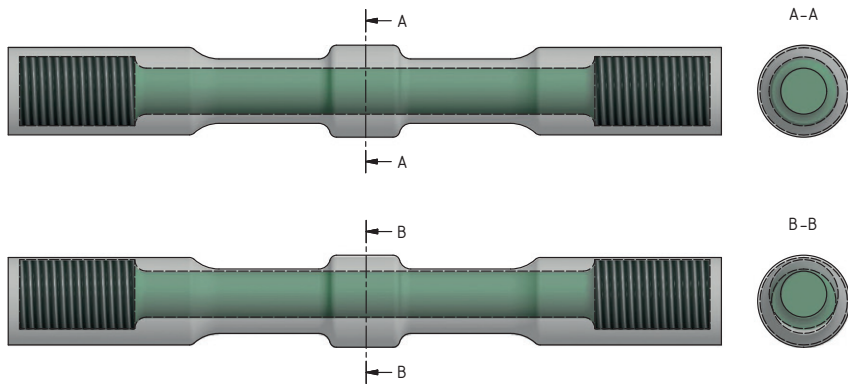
Rundzugstäbe \varnothing 20 mm zentrisch und exzentrisch ausgearbeitet
